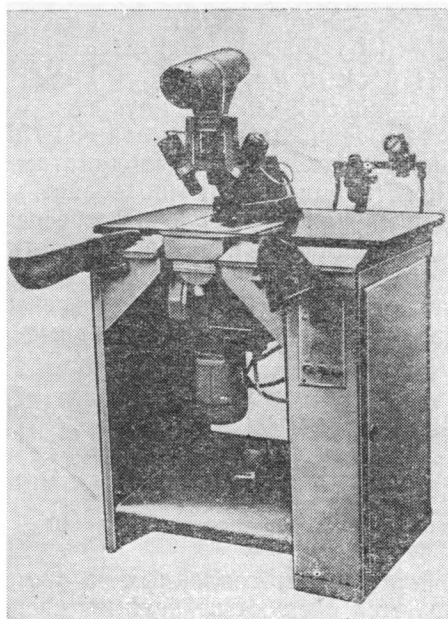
Станок с ручным управлением, оборудованный оптическим устройством и съемным щупом для полуавтоматического сверления
